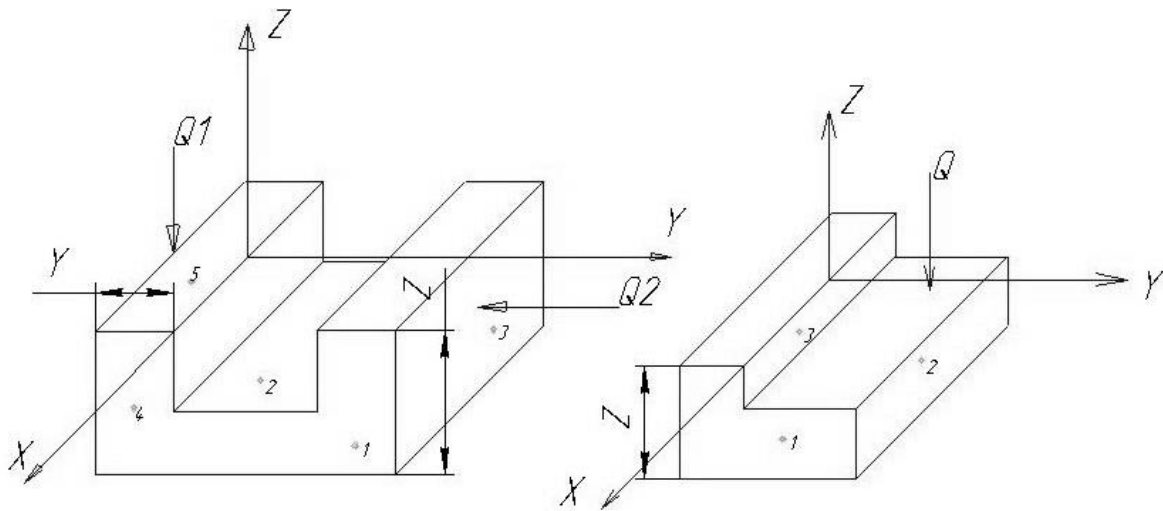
Базування призматичної деталі з усуненням 5-ти чи 3-х ступенів свободи
